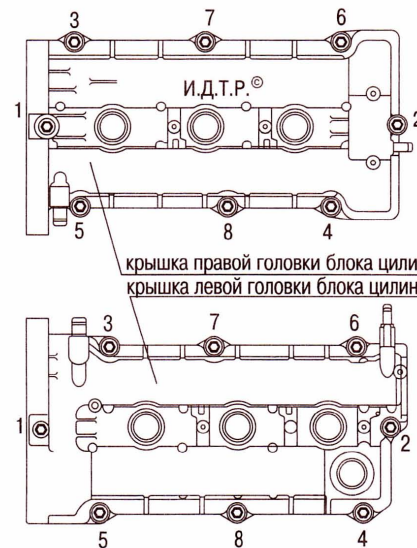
Болты крепления крышек головок блока цилиндров
